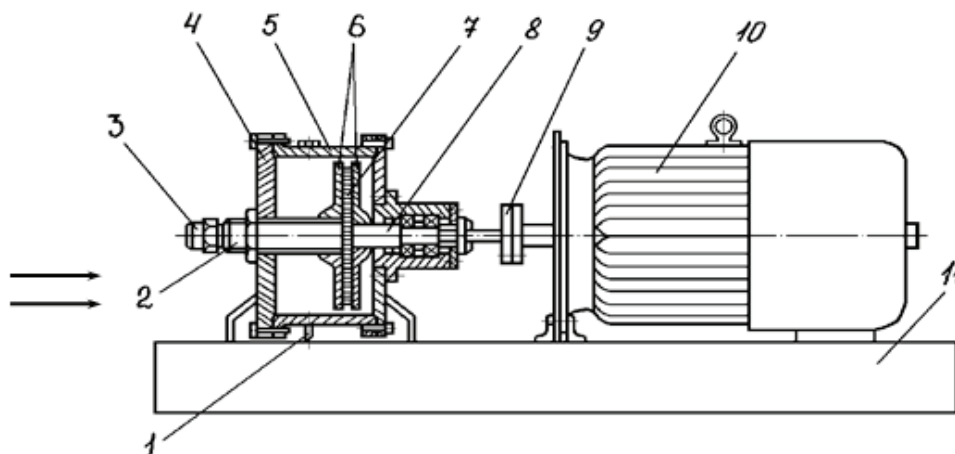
Стенд для приготовления ВТЭ: 1 — сливное отверстие; 2 — полый вал; 3 — подача воды и топлива; 4 — корпус; 5 — дисмембратор; 6 — диски; 7 — штифты; 8 — вращающийся вал; 9 — муфта; 10 — электродвигатель; 11 — рама
